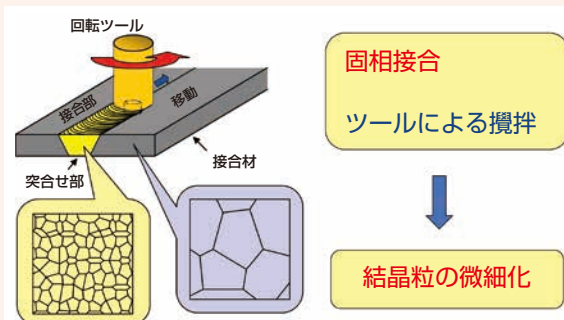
摩擦攪拌接合(Friction Stir Welding)
